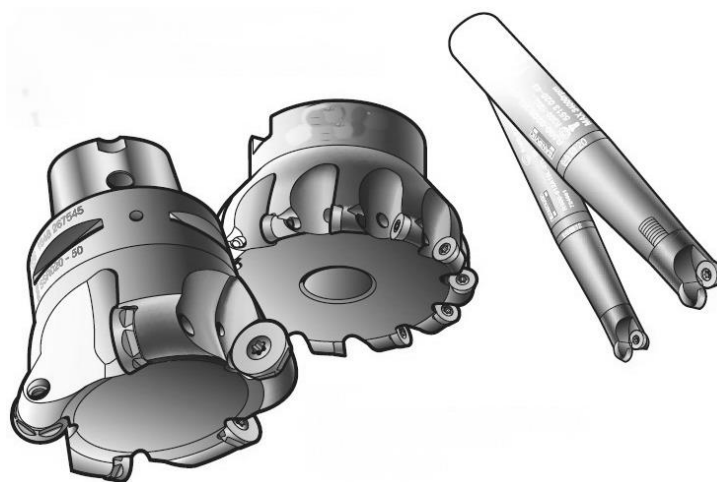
Загальний вигляд типових конструкцій фрез із круглими ріжучими пластинками
